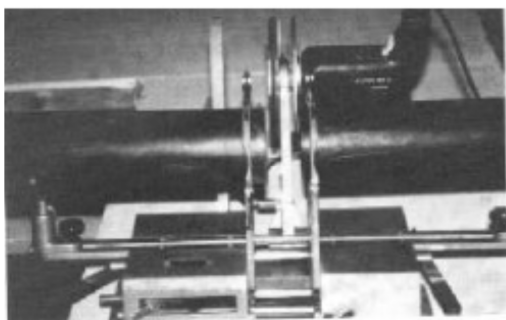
Soldadora de tubo em polietileno.
